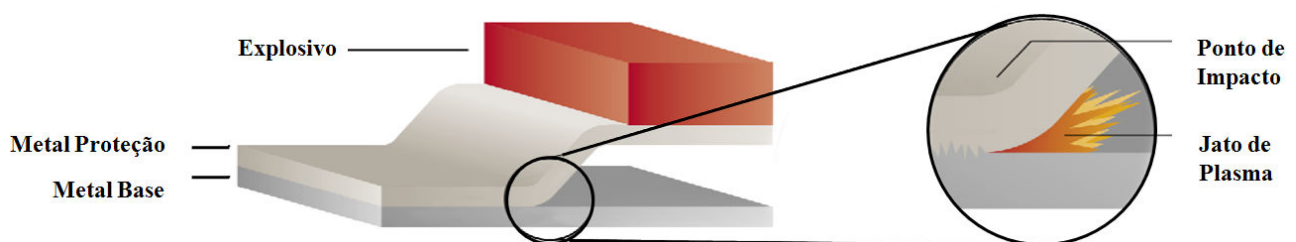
Fabricação de chapa cladeada com soldagem por explosão (PA&E, 2006).
